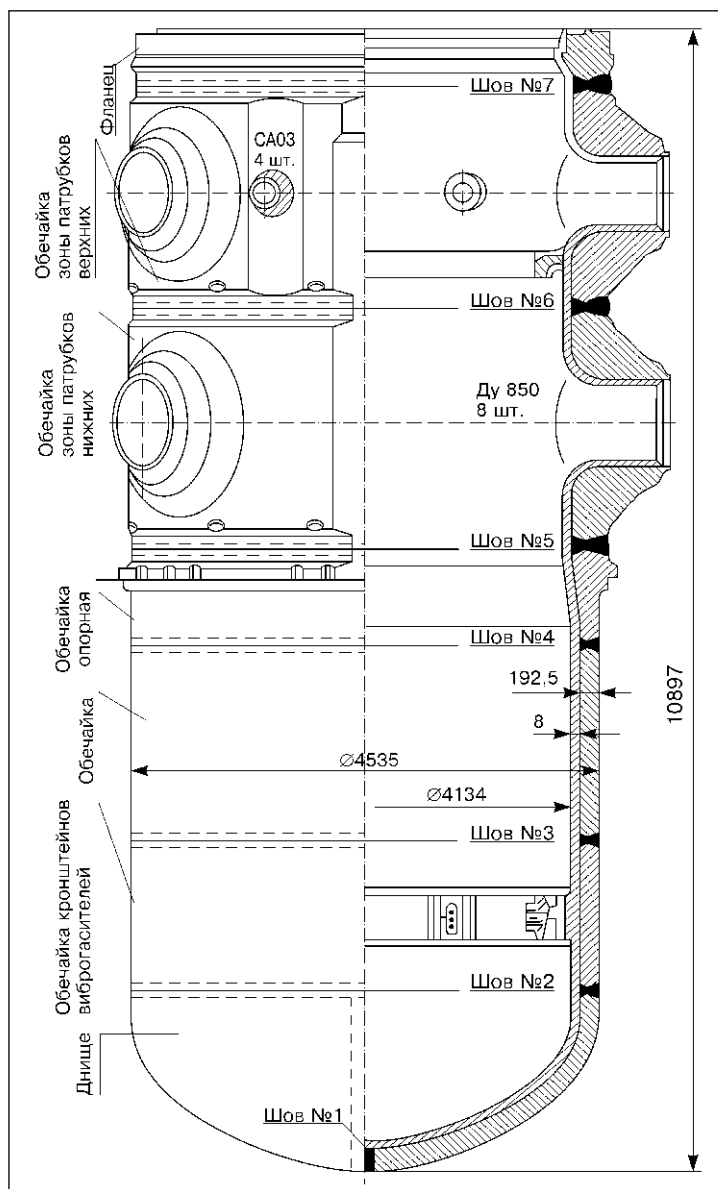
Сварной корпус реактора (нижняя часть) ВВЭР-1000
